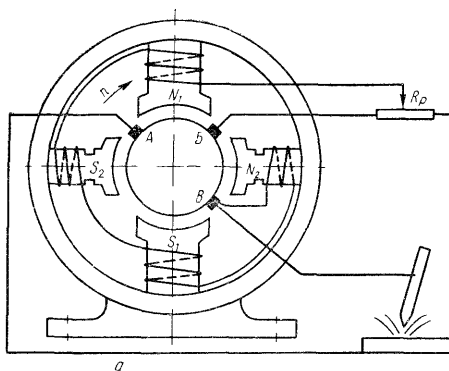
Сварочный генератор с расщепленными полюсами:
